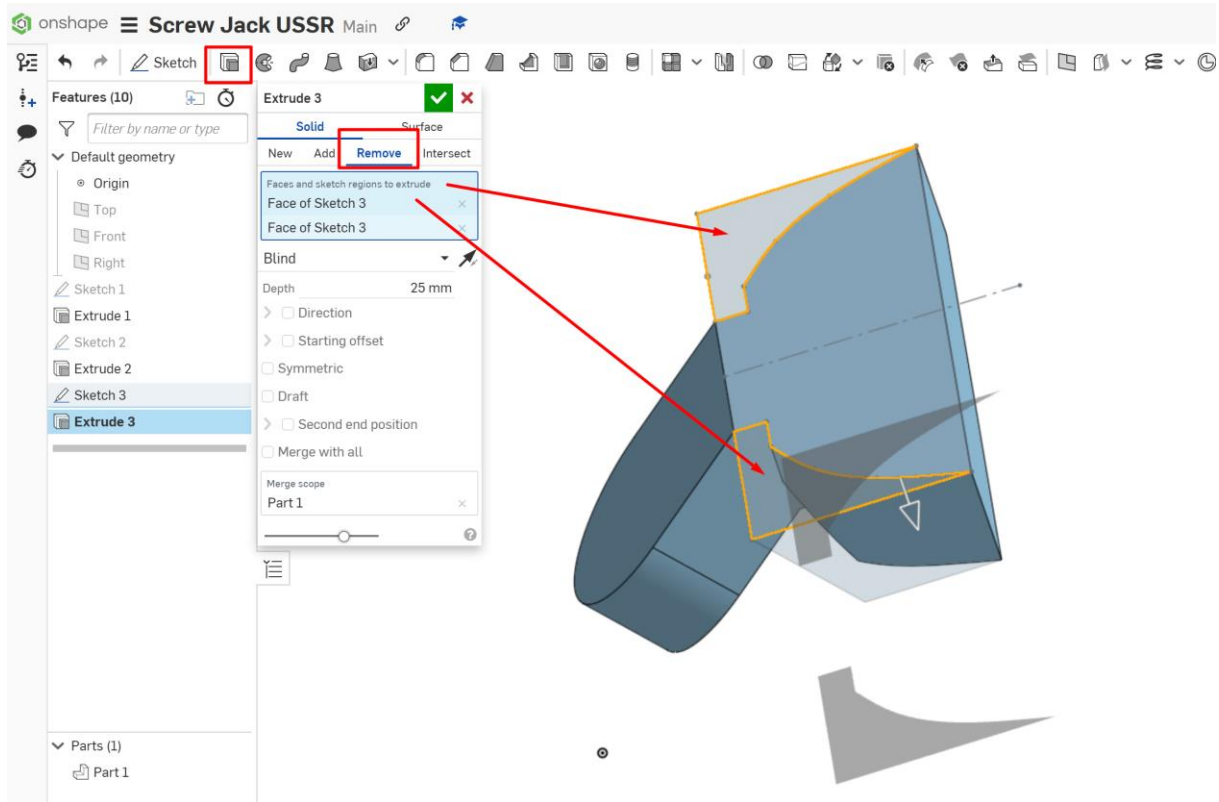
Формування робочого контуру верхньої частини операцією вирізання
